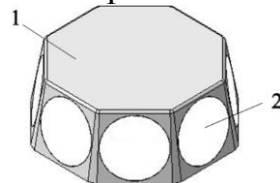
Круговий світлоповертальний елемент: 1- корпус світлоповертального елемента; 2 - світлоповертальний мікропризмовий елемент
